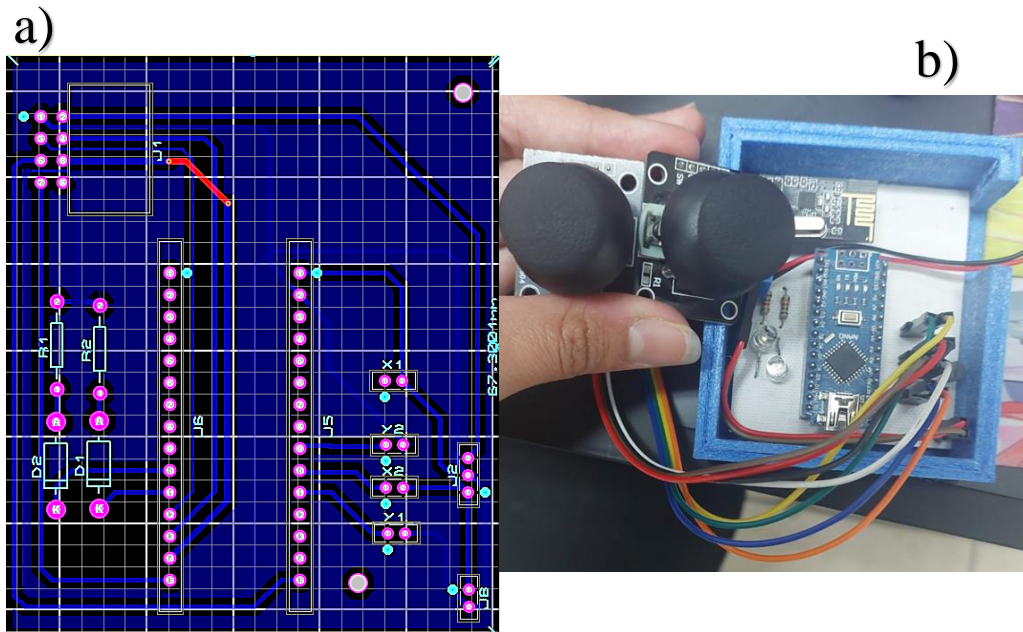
a) PCB del control remoto, b) PCB física del control remoto
